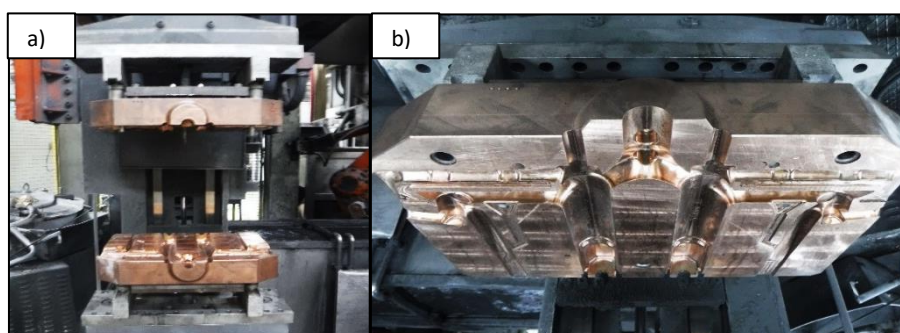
a) Molde montado; b) Detalhe a coquilha (sem macho inserido).
